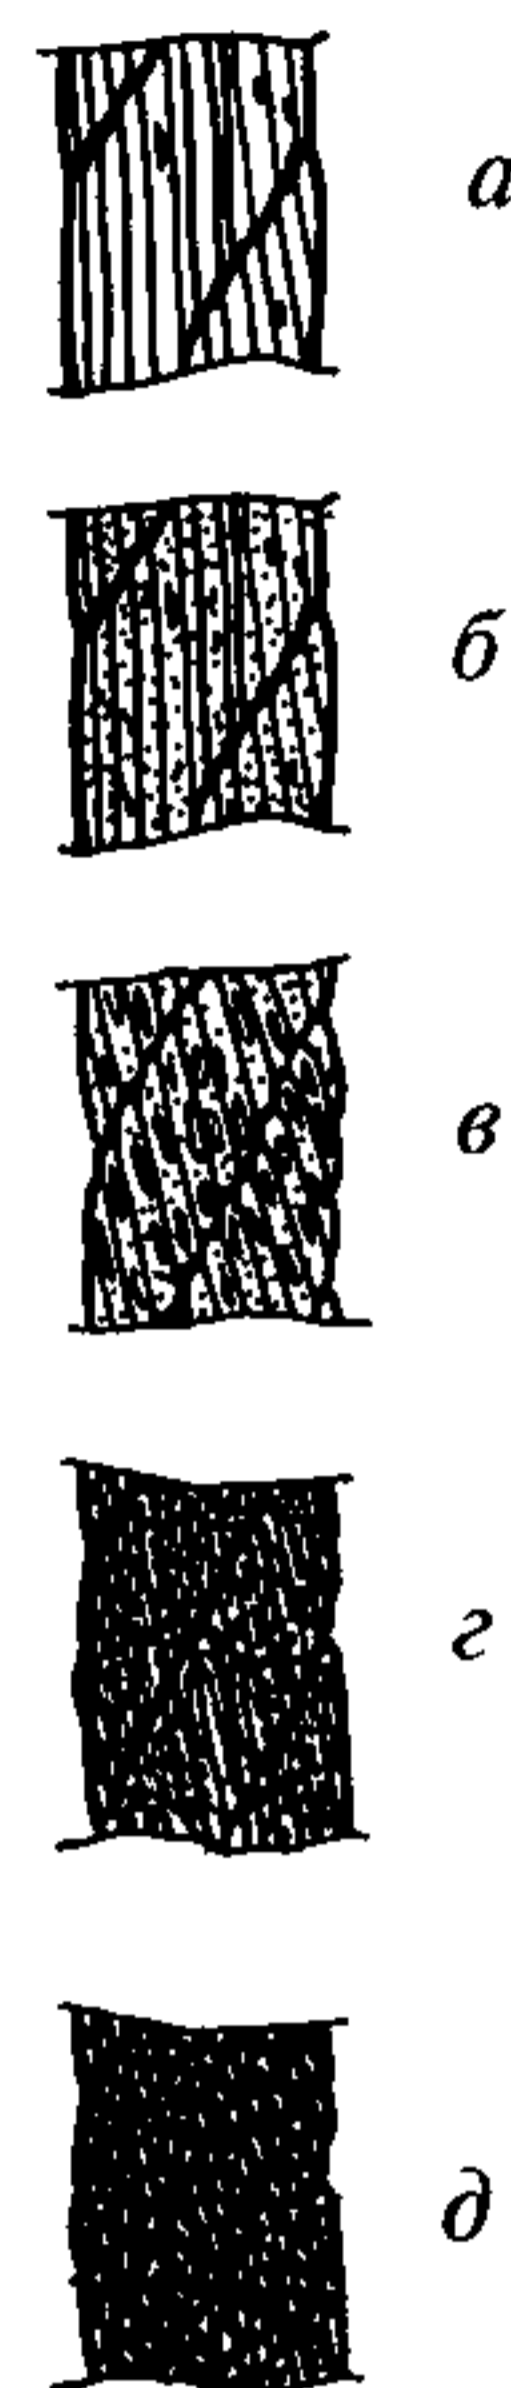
Поверхностная коррозия проволок каната крестовой свивки:
